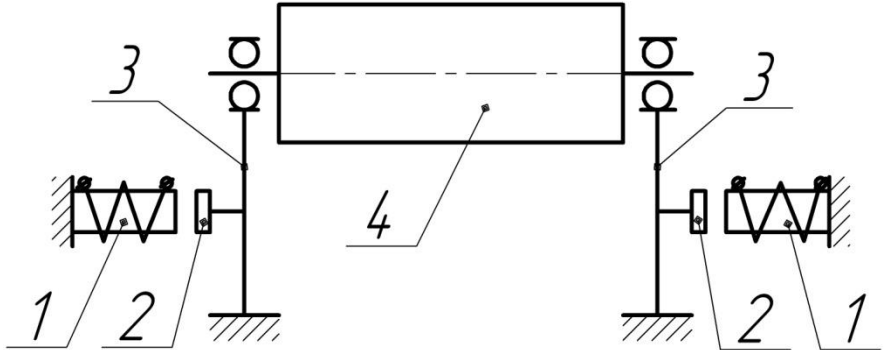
Схема станда для статичного балансування ротора із підшипниковими опорами і накладеними вібраціями: 1 – електромагніт; 2 – якор; 3 – опори станда із підшипниками; 4 – ротор
